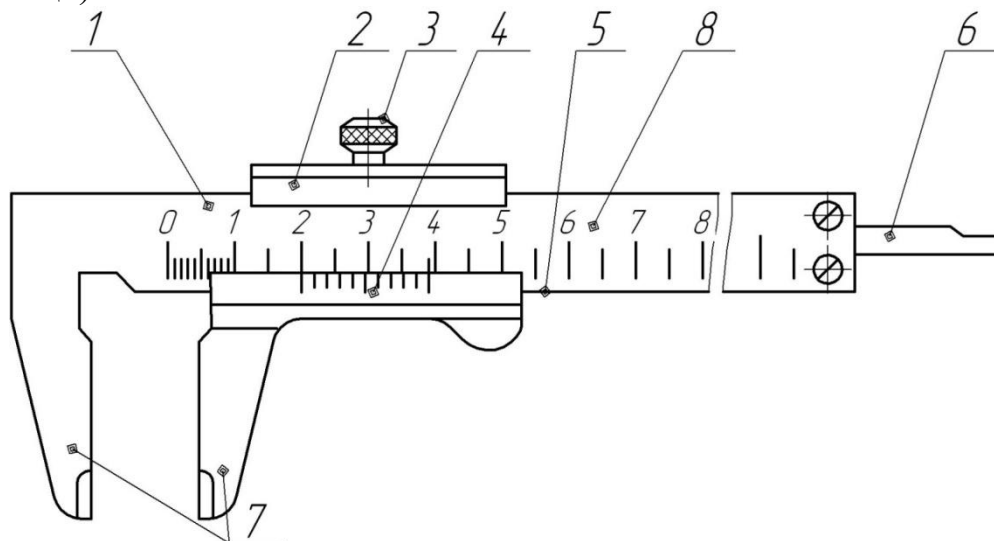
Конструкція та будова штангенциркуля ШЦТ-I: 1 – штанга; 2 – рамка; 3 – фіксатор; 4 – ноніус; 5 – робоча поверхня штанги; 6 – глибиномір; 7 – губки з плоскими вимірювальними поверхнями для вимірювання зовнішніх розмірів; 8 – шкала штанги
